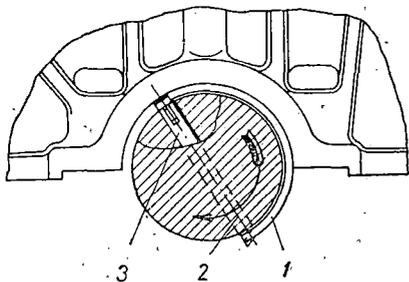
Удаление верхнего вкладыша коренного подшипника:
